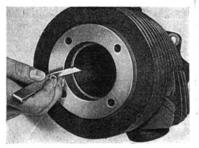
Messen des Kolbenring-Stohmaßes mittels Fühllehre
